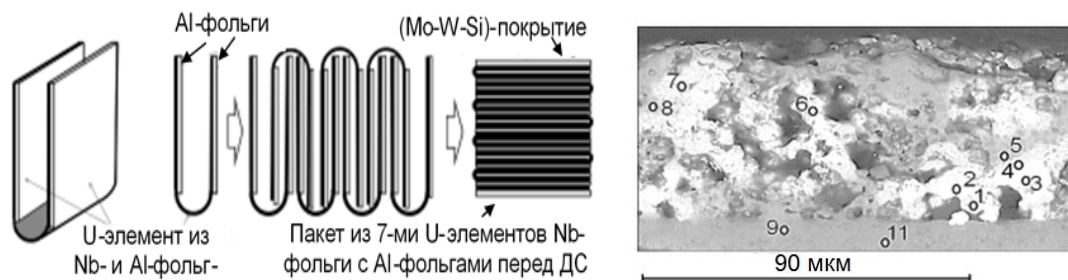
U-элемент из Nb-фольги с Al-фольг, схема сборки многослойного пакета и пакет из U-элементов с покрытиями, подготовленный к ДС
